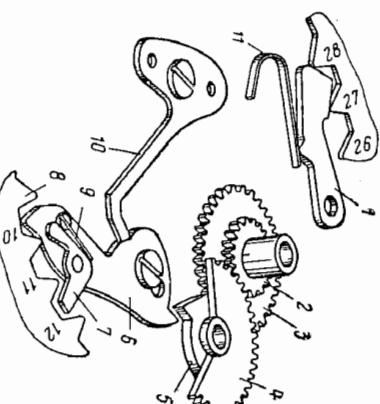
Кинематическая схема календарного устройства часов «Слава» 2414:
